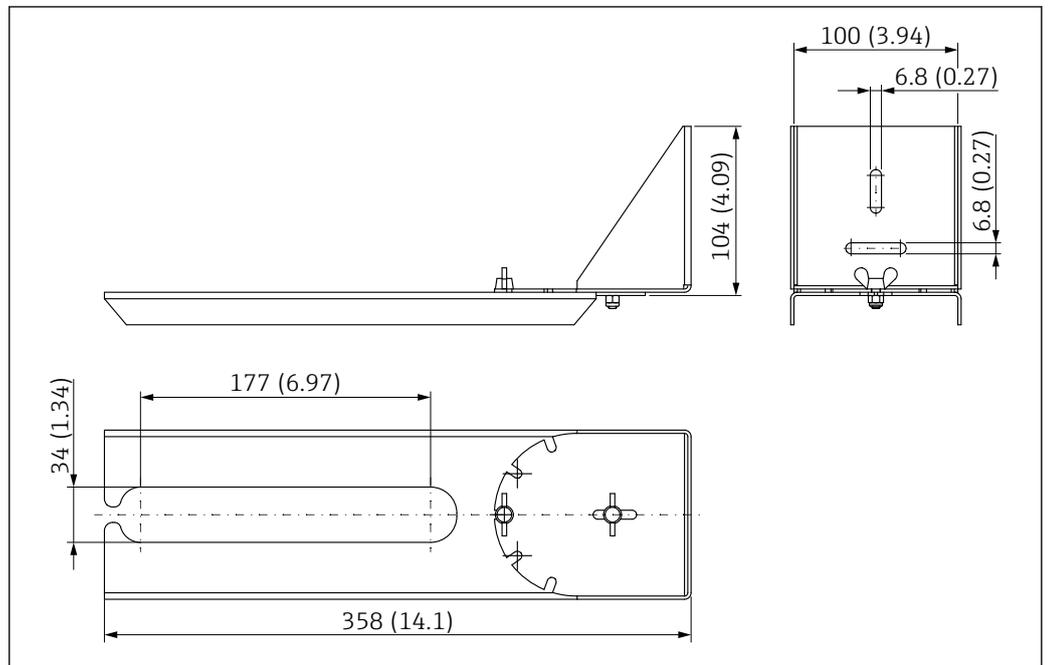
Dimensões do suporte de montagem pivotável. Unidade de medida mm (in)
